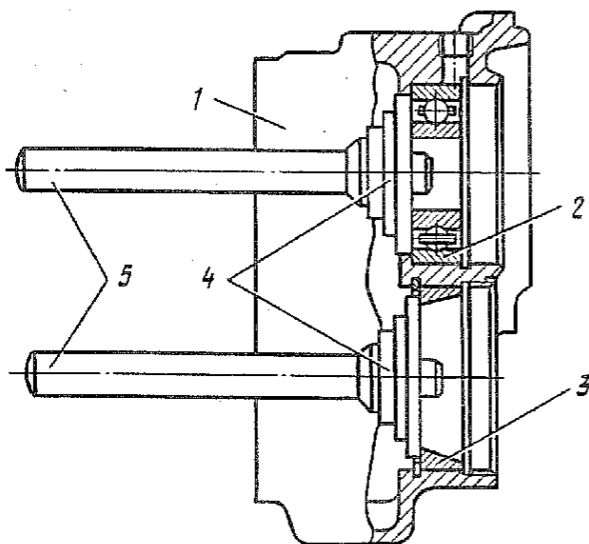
Выпрессовка внутренних подшипников колесного редуктора:
